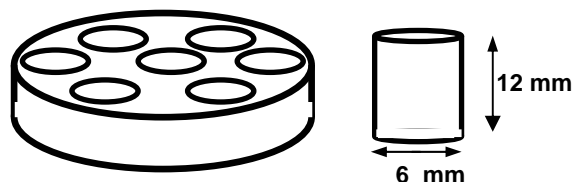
Molde y probeta de ensayo mecánico de compresión.
